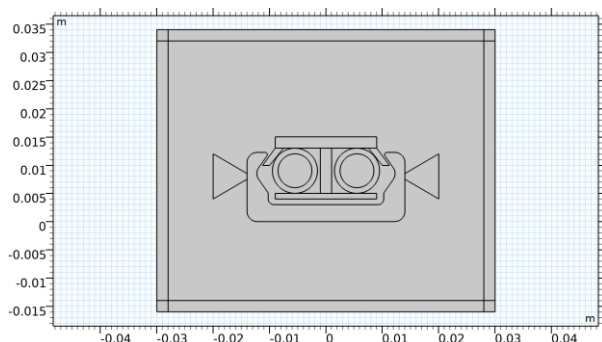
Итоговая конструкция индуктора с закаливаемой деталью
